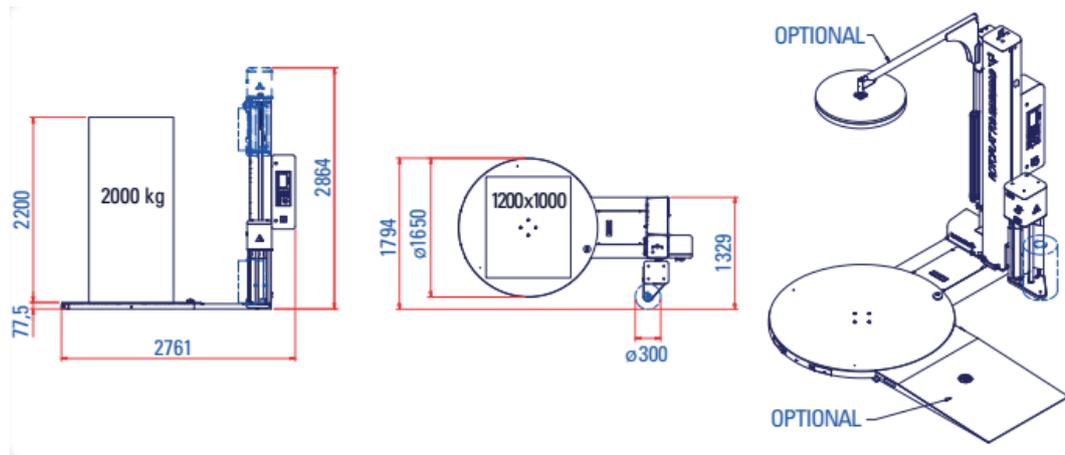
Dimensiones de la máquina envolvedora Robopac Rotoplat 508
